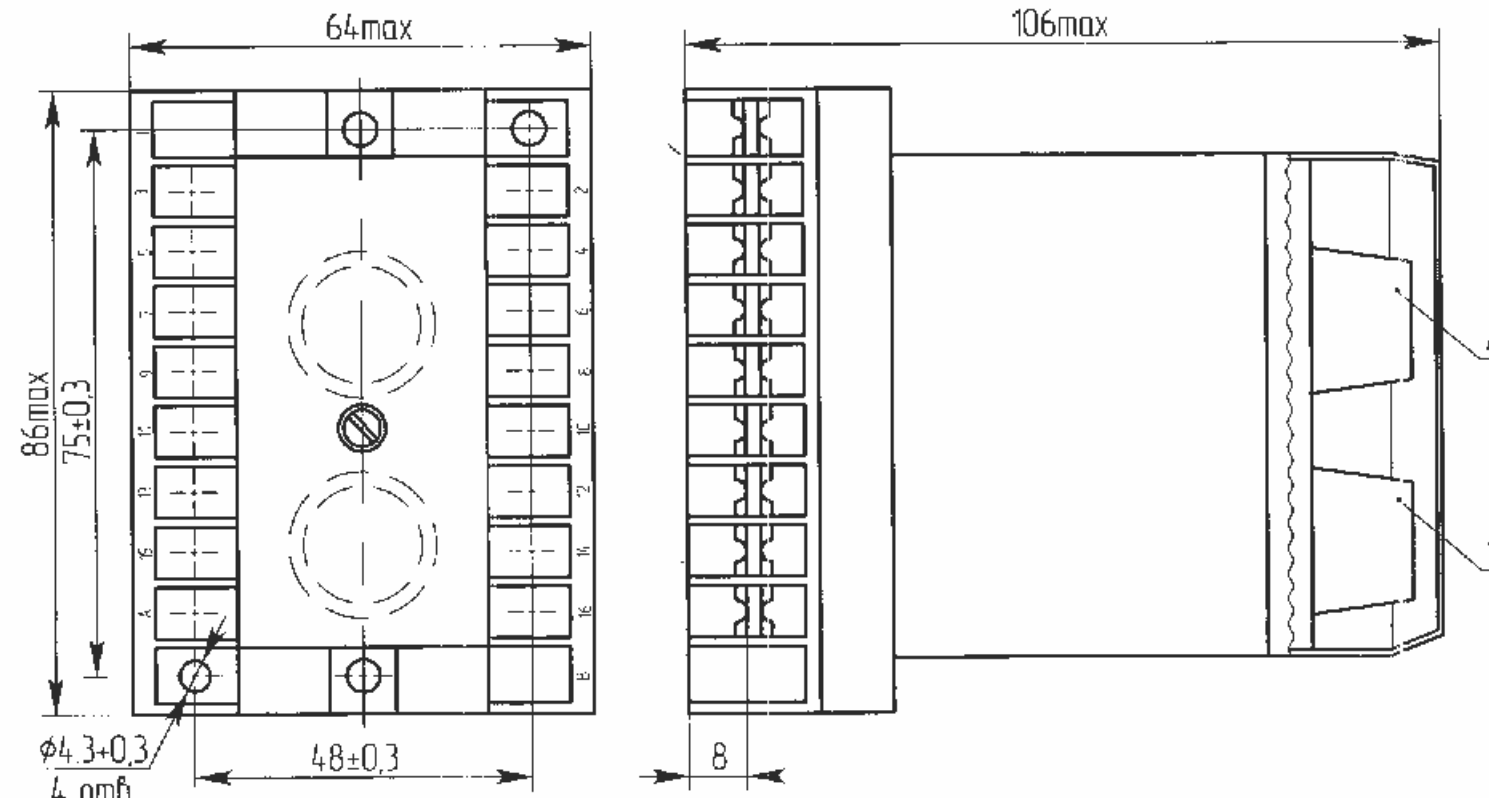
Реле типов PCB18-13-XXXX1, PCB18-23-XXXX1, PCB18-13-XXXX2, PCB18-23-XXXX2
